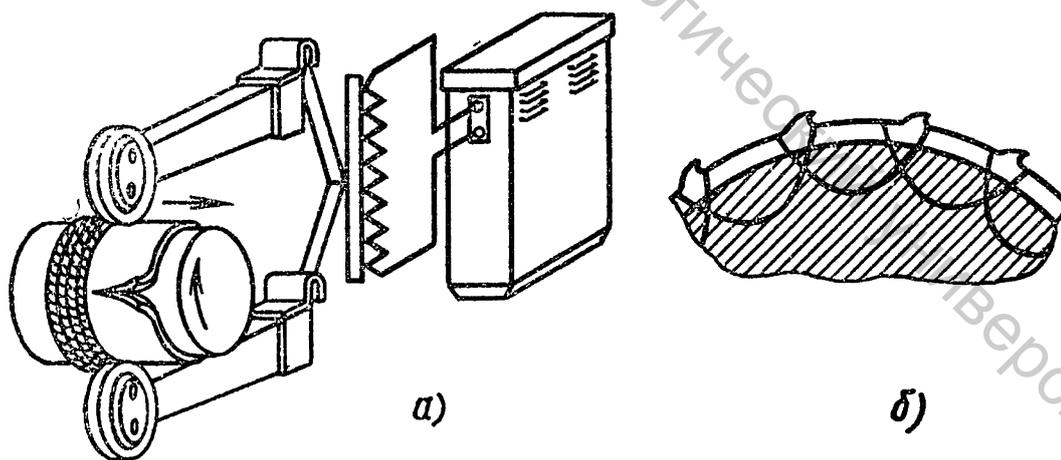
Схема приварки металлической ленты к поверхности вала:
